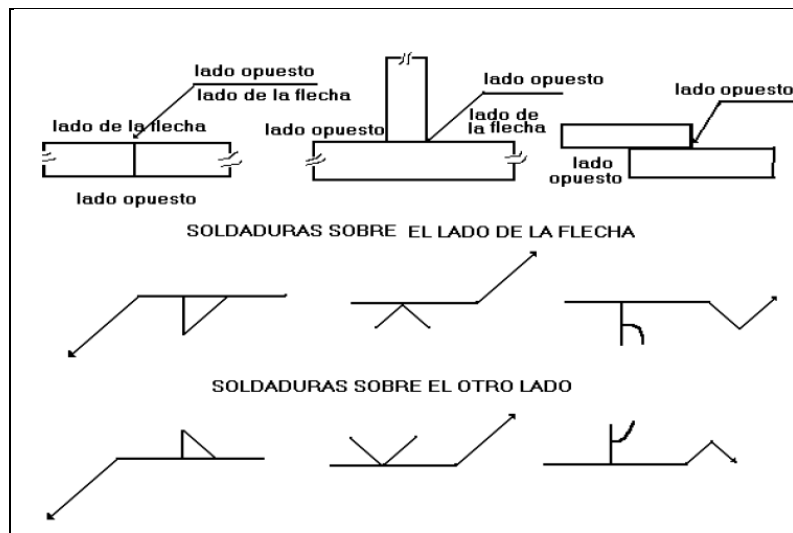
Símbolos básicos en la representación de soldadura
